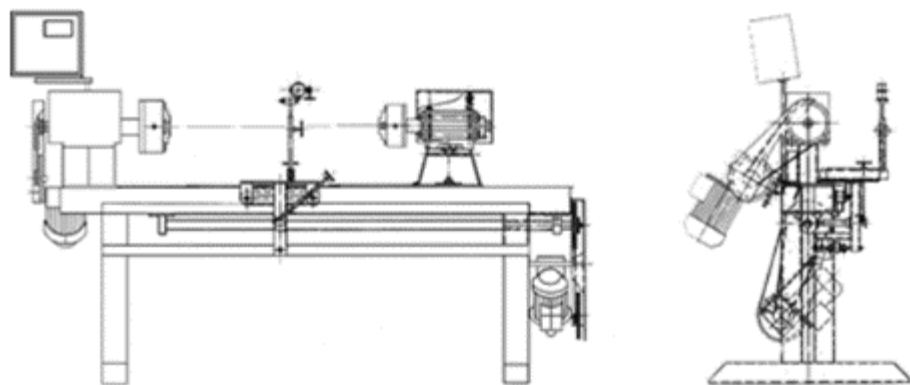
Пристрій для наплавки валів марки СУН-01
